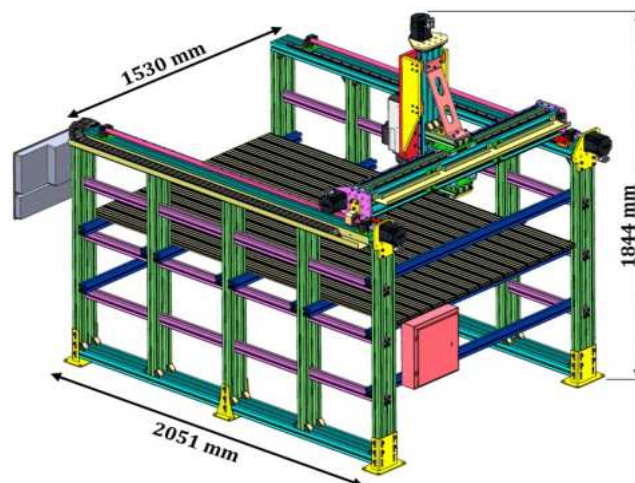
Vedere izometrică din spate cu dimensiunile de gabarit
